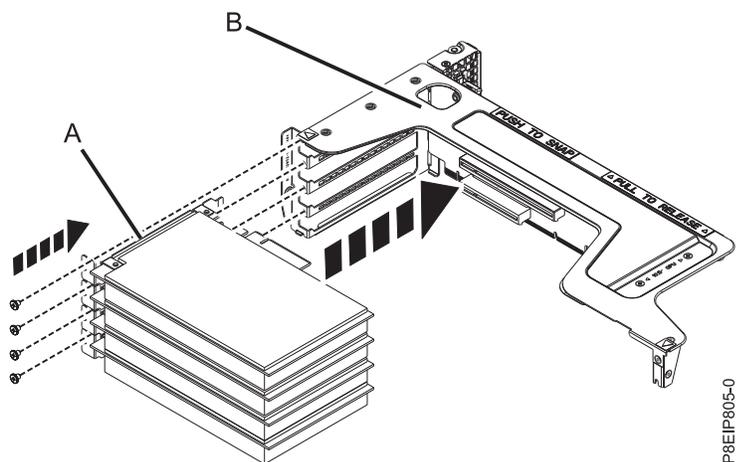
Inserción de un adaptador PCIe en la tarjeta de expansión
